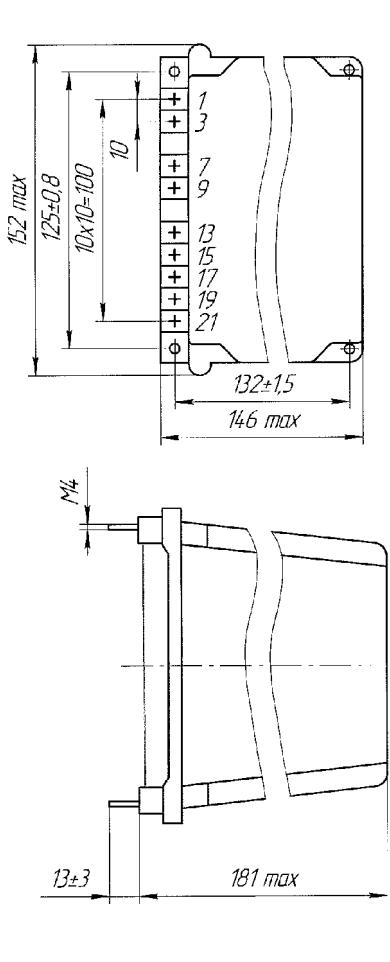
Габаритные, установочные и присоединительные размеры реле типа РГР 11.
